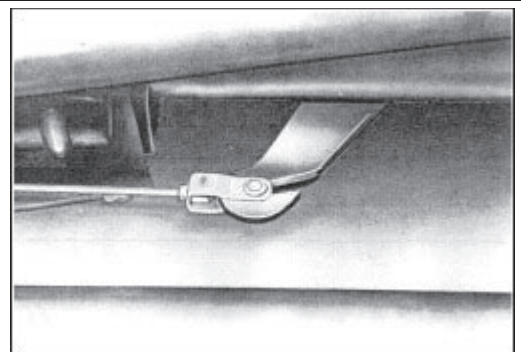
Befestigung des vorderen Seilzuges am Handbremshebel
